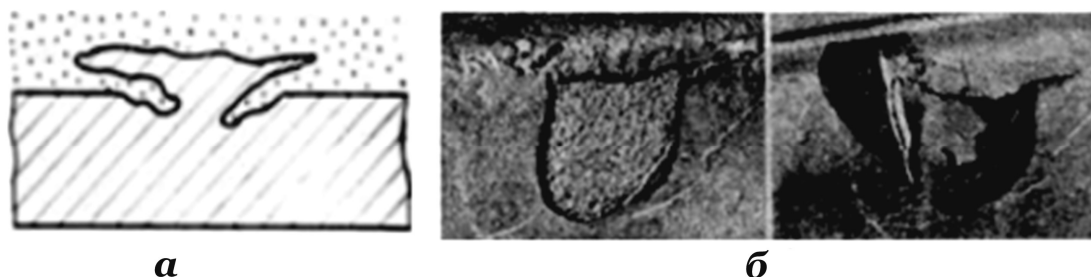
Дефект – ужимина: а – схема; б – дефектные отливки
